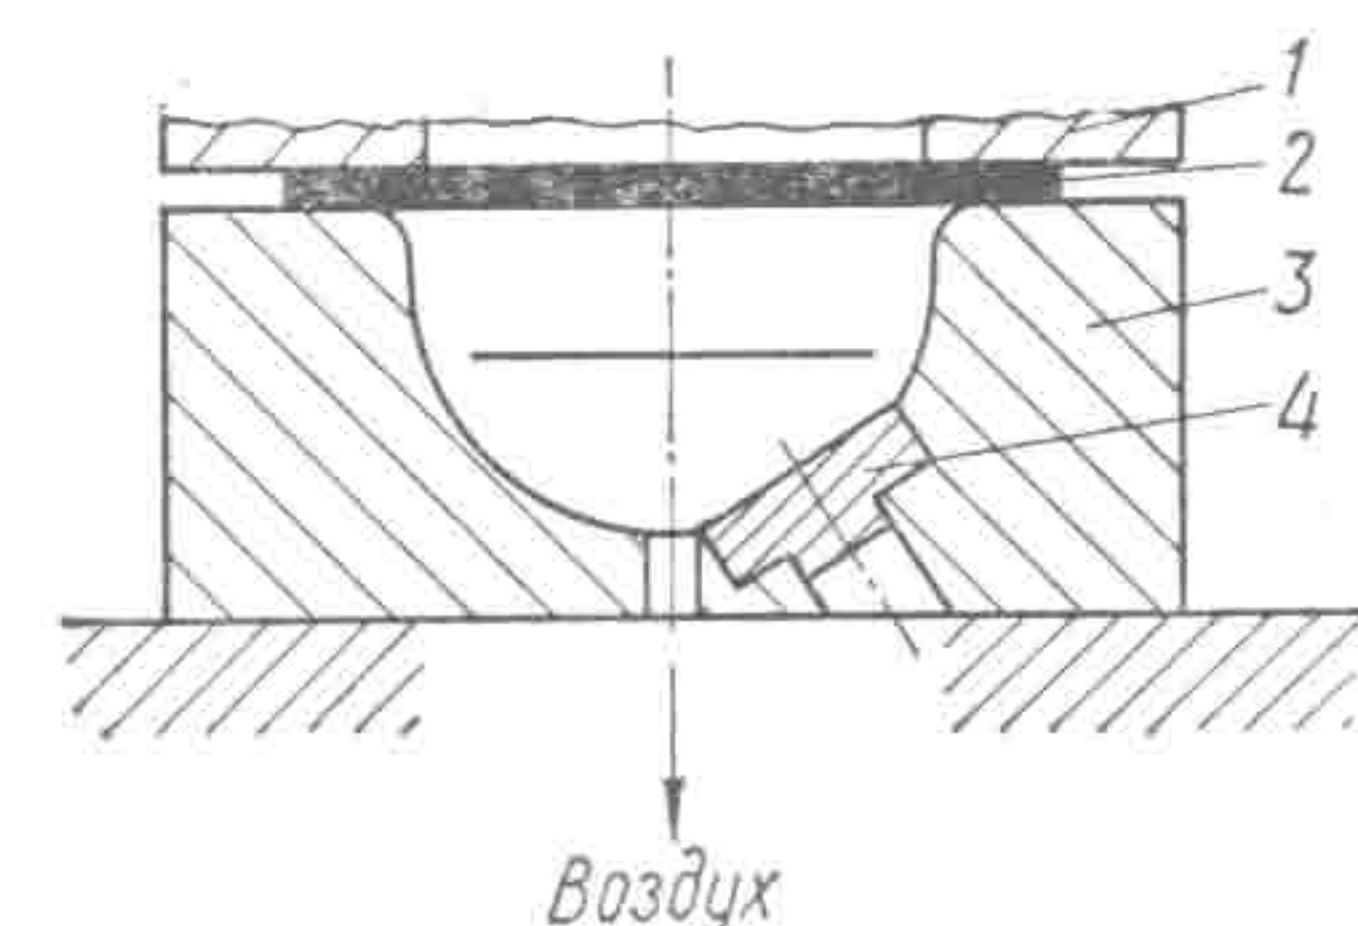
Схема оснастки для вытяжки с последующей пробивкой:
